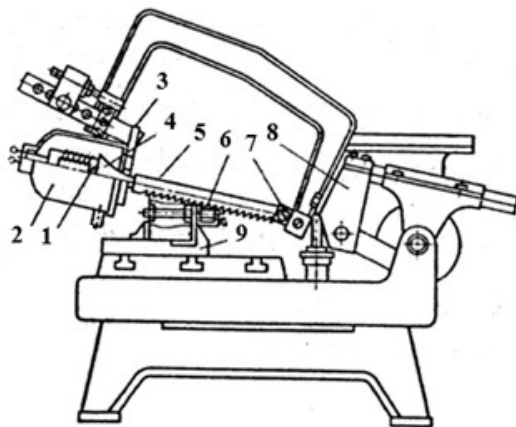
Компоновка узлов ножовочного станка для разрезания заготовок с ультразвуком : 1 – магнитострикционный преобразователь; 2 – резервуар; 3 – опорная плита; 4 – концентратор колебаний; 5 – ножовочное полотно; 6 – обрабатываемая деталь; 7 – винт; 8 – опорная стойка; 9 – тиски
